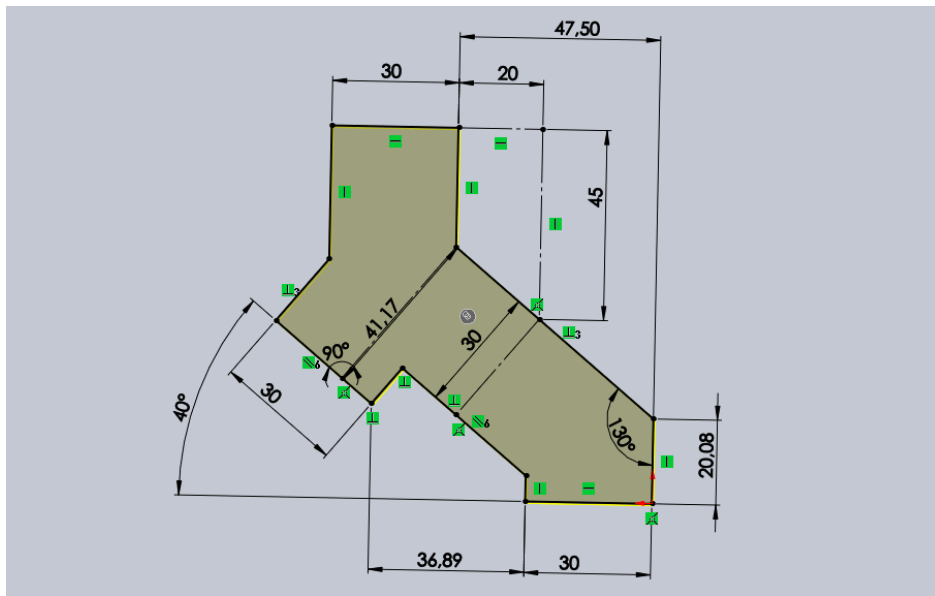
Extrusión desde su croquis con una altura de 20mm.
